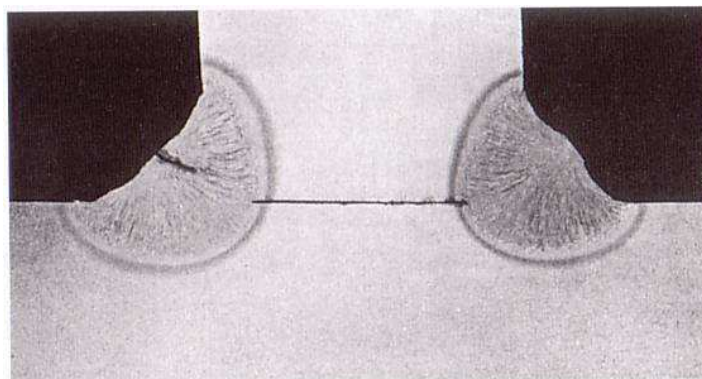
Erstarrungsriss in Stahlschweißgut [21]
